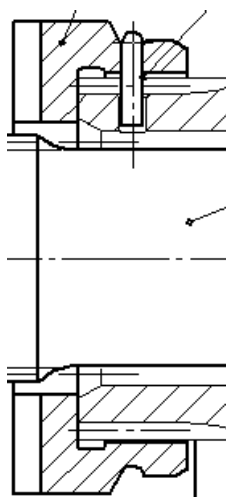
Общий вид шлицевого соединения полумуфты блокировки межколесного дифференциала и корпуса дифференциала
